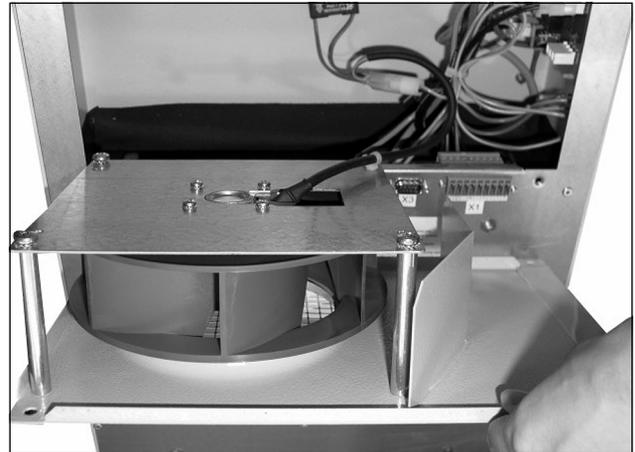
Ôter la plaque de recouvrement intégrant le ventilateur
